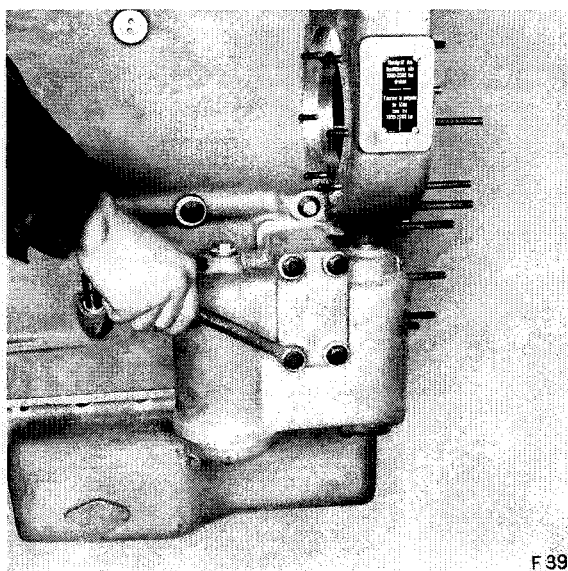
Entfernen der Ölleitung zwischen Luftkompressor und Motorgehäuse
